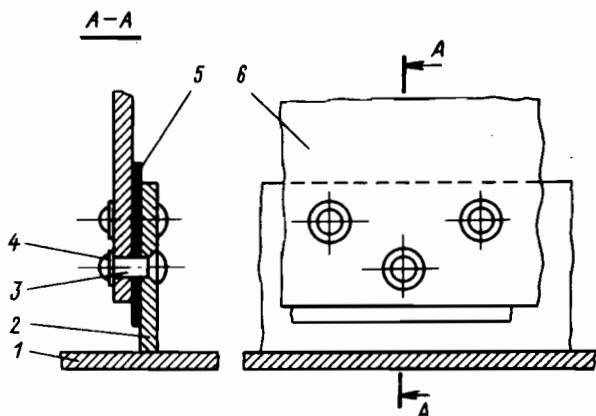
Соединение конструкций надстройки из алюминево-магниевого сплава со стальным корпусом.
